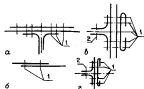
Схемы образцов прочных угловых и стыковых соединений деталей, узлов, секций ГО между собой: а - угловое стыковое соединение с усилением; б - стыковое соединение выхлест с прошивкой; в - угловое соединение лентой с косингсом и с усилением; г - угловое соединение лентой с косингсом без усиления; 1 - прошивка; 2 - ось отверстия под болт
